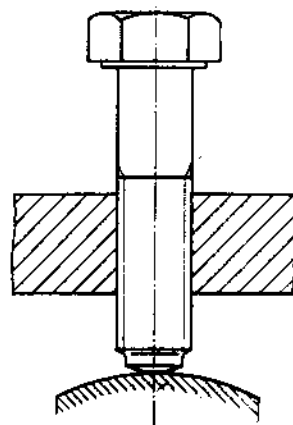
Collegamento con vite ad estremità a calotta. Dal contatto vite-pezzo gli sforzi si trasmettono ai fianchi dei filetti del sistema vite-madrevite.
